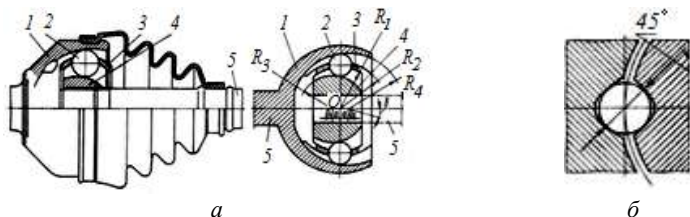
Шестикульковий карданний шарнір з ділильними канавками (типу «Бірфільд»): *а* – конструкція; *б* – схеми; 1 – корпус; 2 – кульки; 3 – сепаратор; 4 – кулачок; 5 – вал
